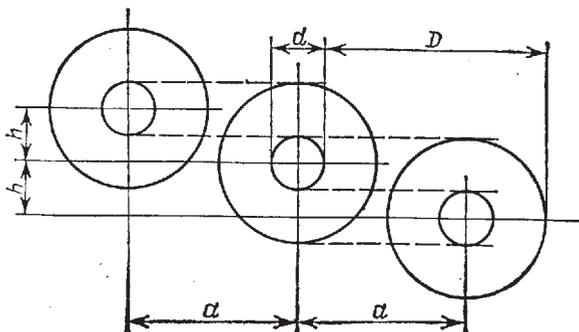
Расположение отпечатков факелов при окрашивании центробежными распылителями в электростатическом поле для получения равномерного покрытия
